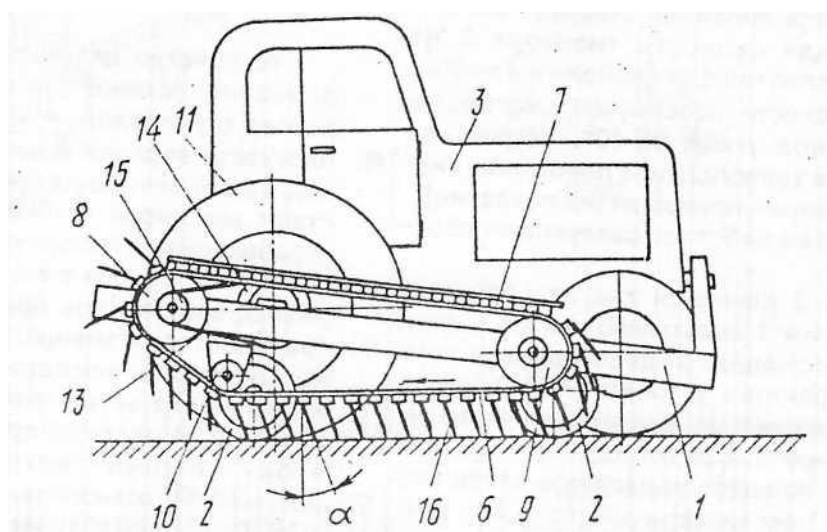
Пристрій для ворущіння валків, вид збоку [10]
